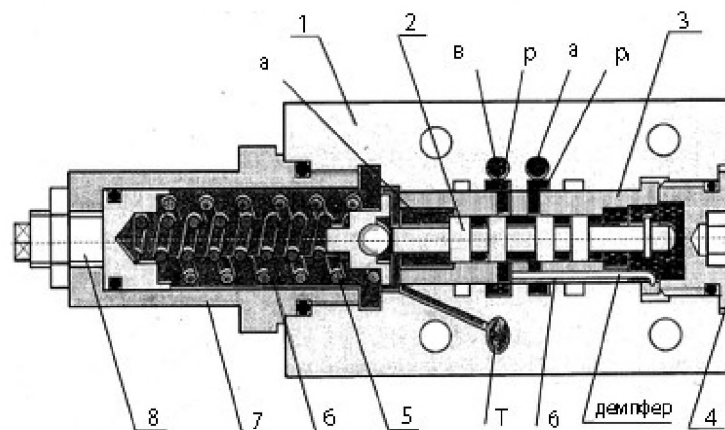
Пристрій трьохлінійного редукційного клапана
